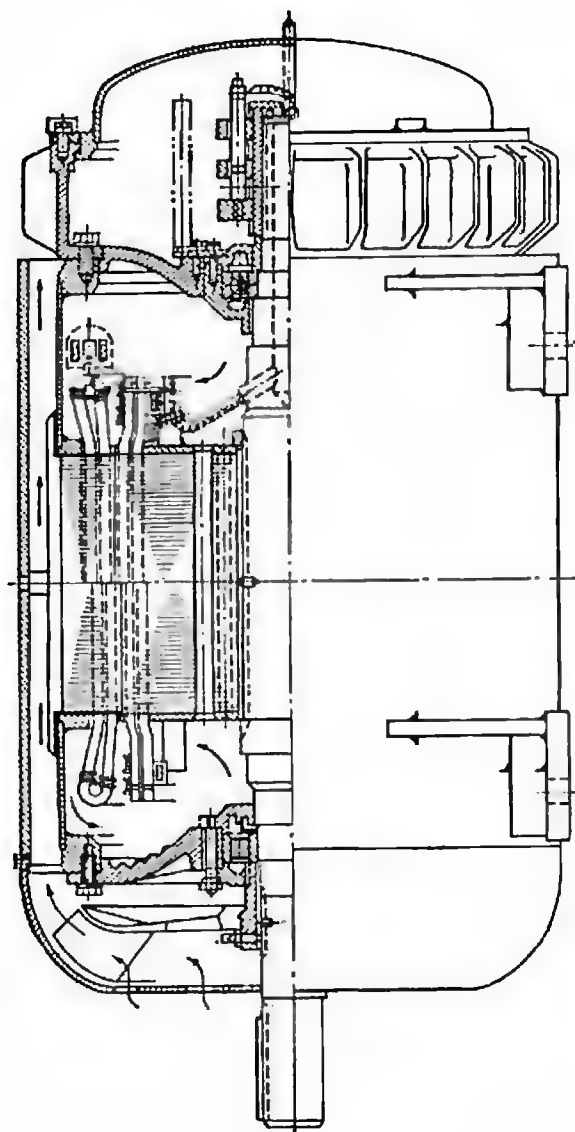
Закрытый обдуваемый двигатель с обрешетчатым корпусом статора и щитами
